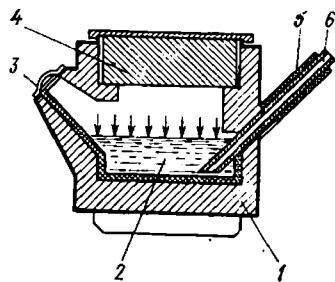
Схема пневматического дозатора для заливки алюминиевых сплавов:
